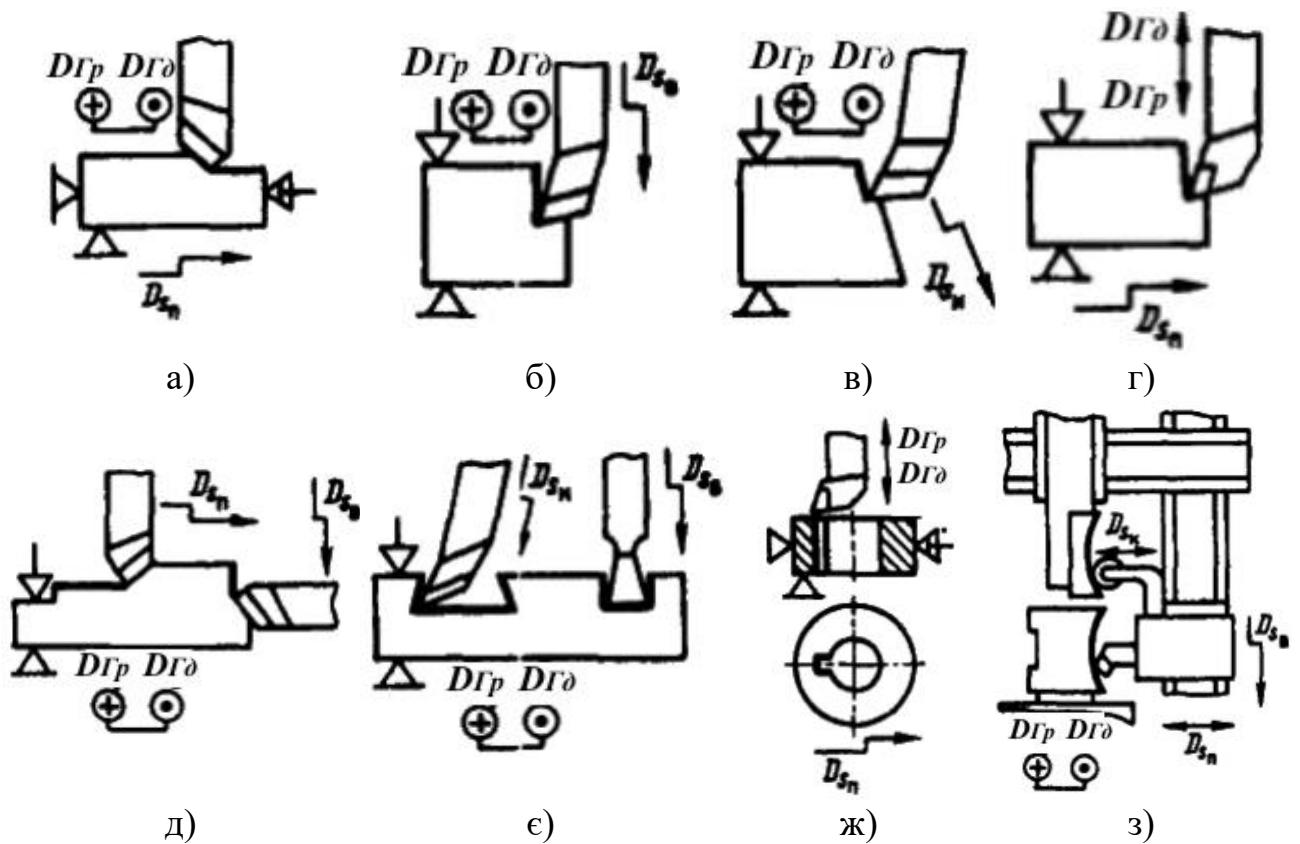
Схеми обробки заготовок на строгальних та довбальних верстатах
